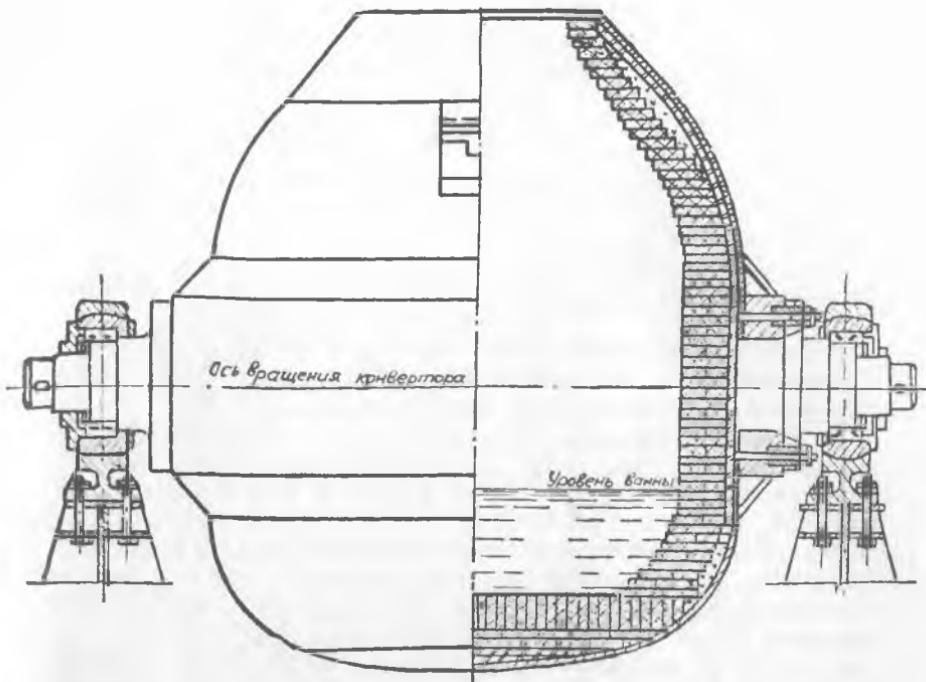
Цельносварной сталеплавильный кислородный конвертор цеха № 2
